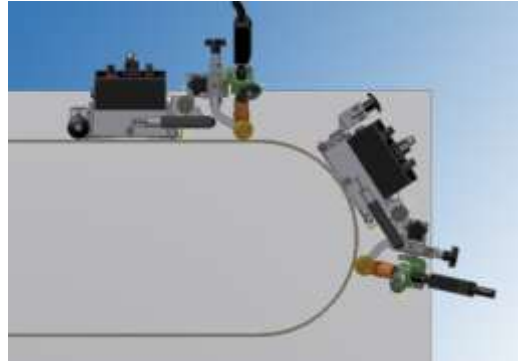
Dikey Tip Köşe Kaynak Robotları [14]
